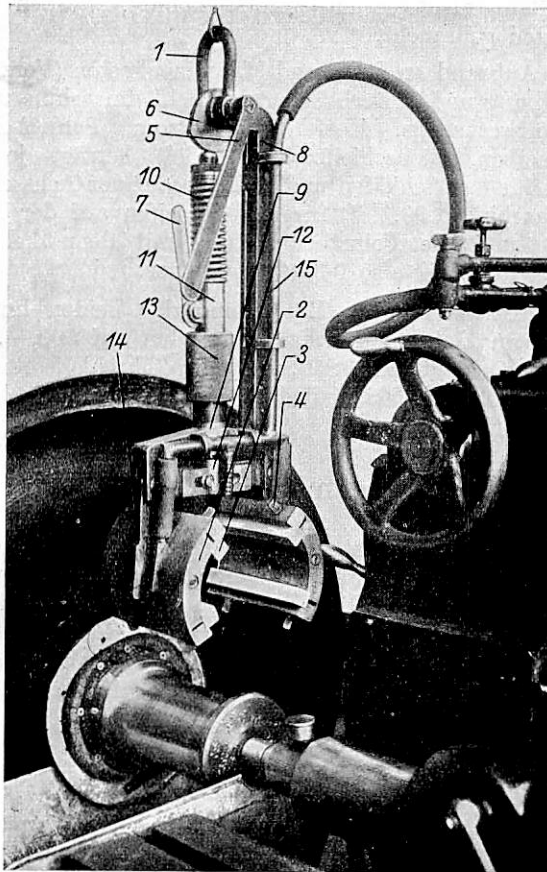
Zieh schleifwerkzeug an einer Achsschenkel schleifmaschine für Wagenradsätze. Werkzeug eingestellt zum Aufsetzen auf den Achsschenkel.
